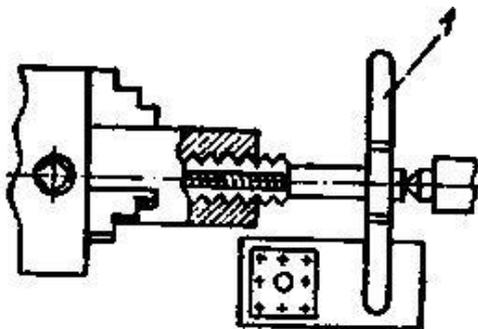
Нарезание резьбы с креплением в слесарном воротке
